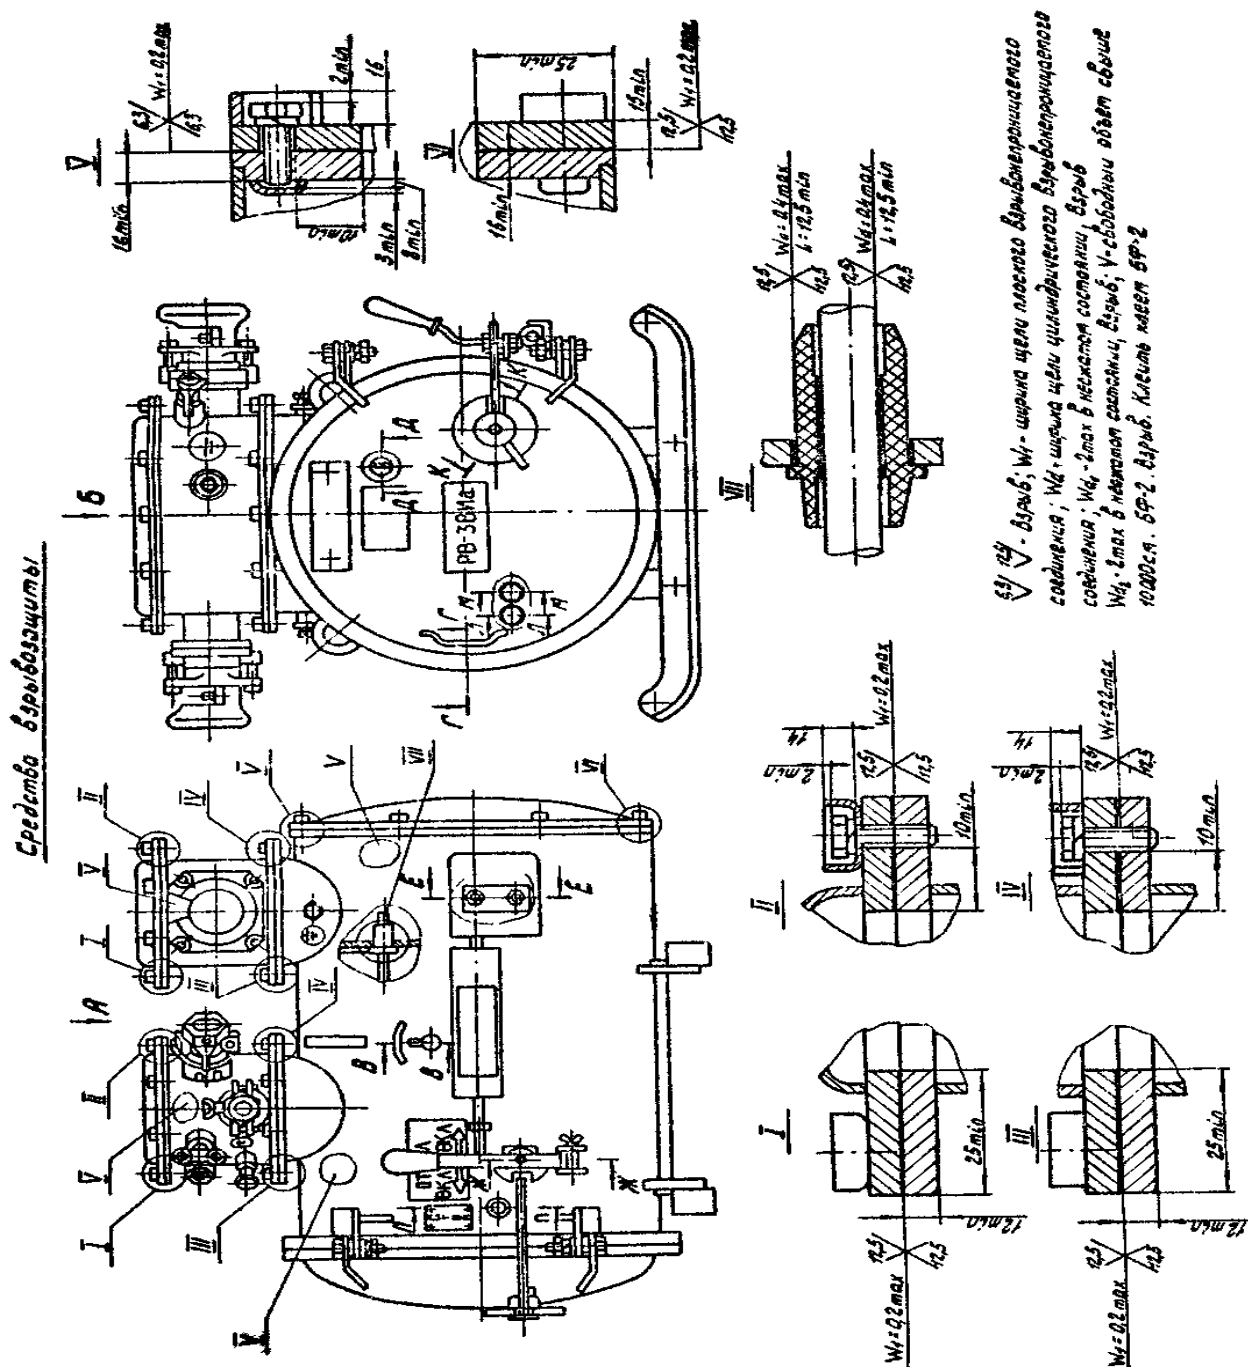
Чертеж взрывозащиты пускателя ПВИ
